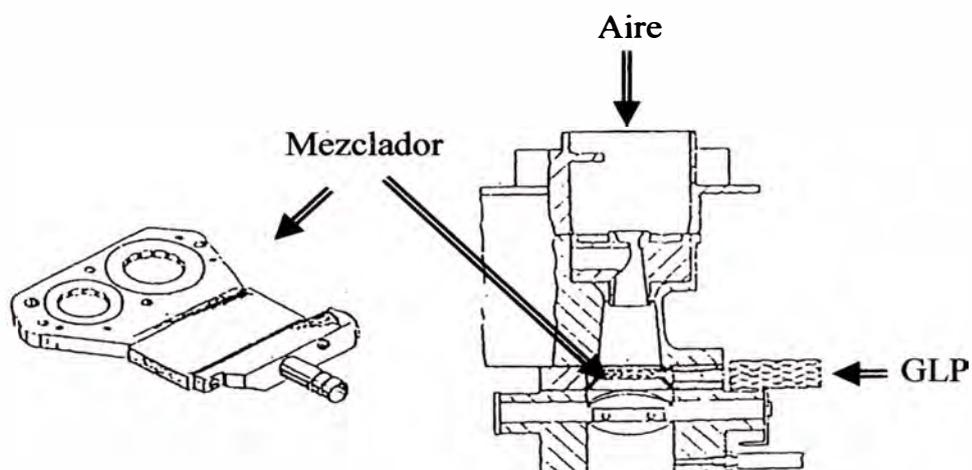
Montaje del mezclador entre el carburador y el cuerpo de la válvula mariposa (carburadores especiales)
